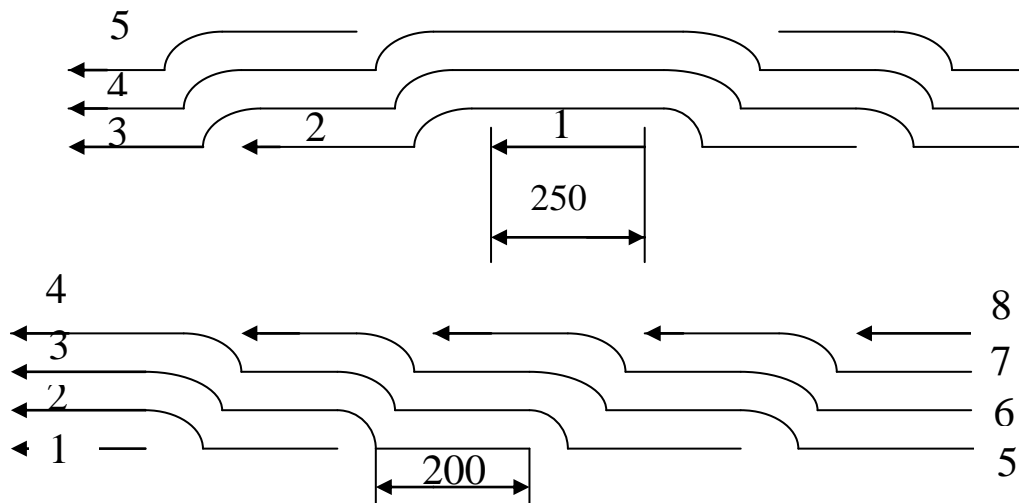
4 – Схеми зварювання довгих багатошарових швів: а – “гірка”; б – “каскад”; 1-8 – послідовність зварювання
